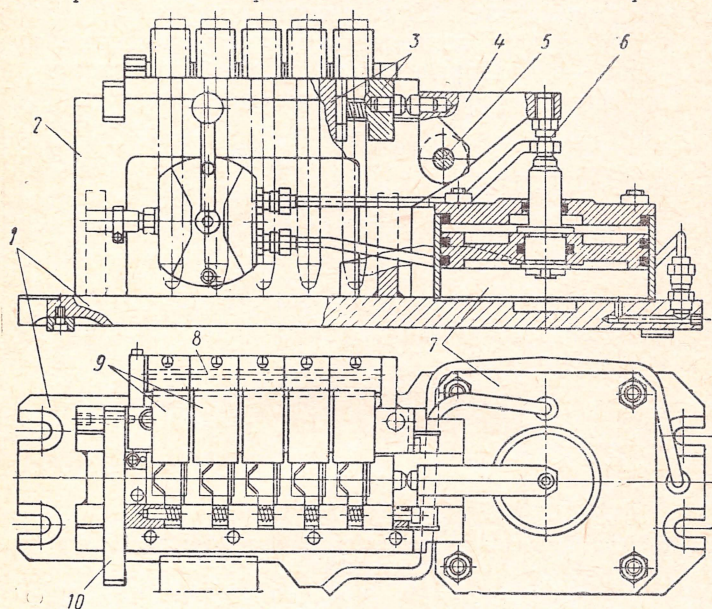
Многоместное пневматическое приспособление для безопасного крепления деталей на фрезерных станках
